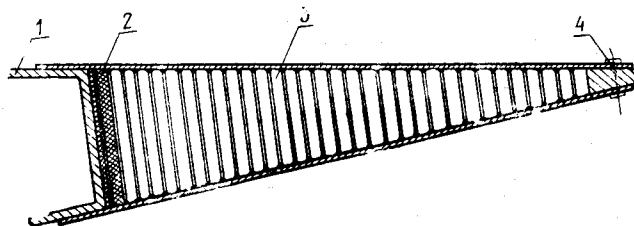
Конструктивная схема соединения обшивок с сотовым наполнителем и элементами каркаса:
